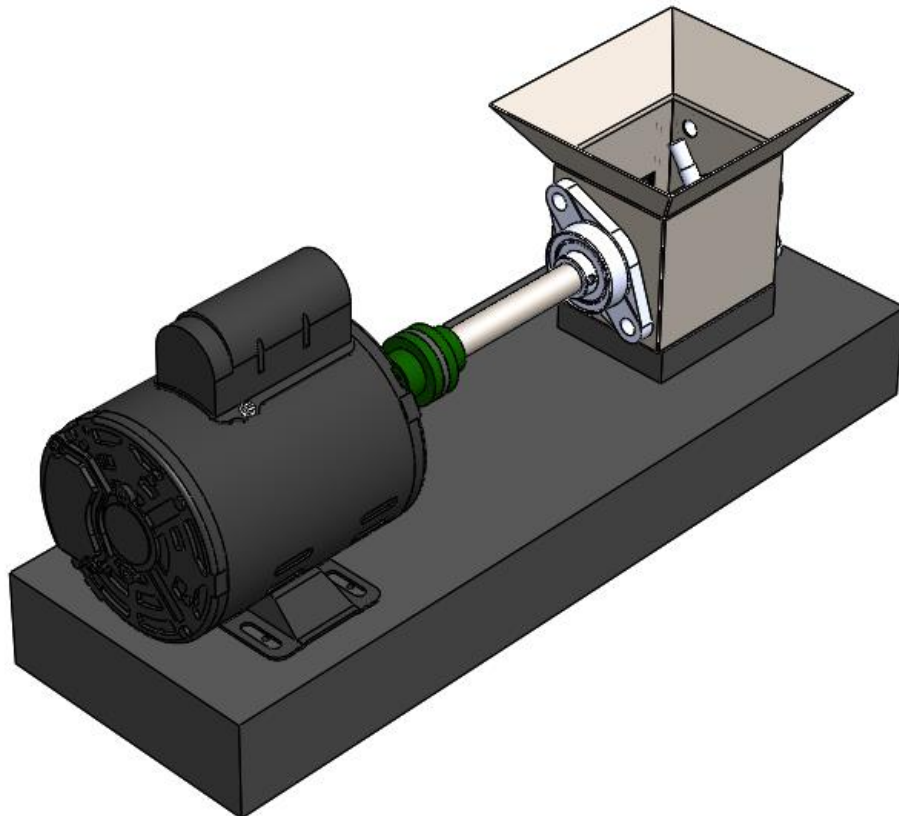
Vista isométrica 3D del equipo diseñado con motivo de la Práctica Profesional Supervisada.
